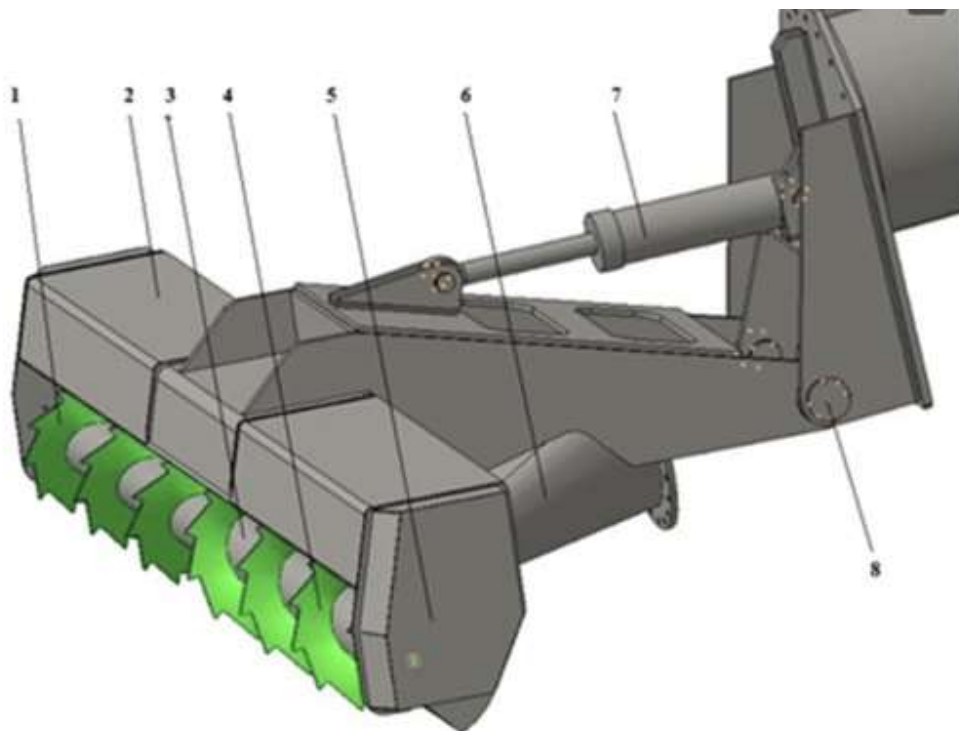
Общий вид грунтозаборного устройства фрезерно-шнекового типа земснаряда гидроАНТ1400/400 [45]
